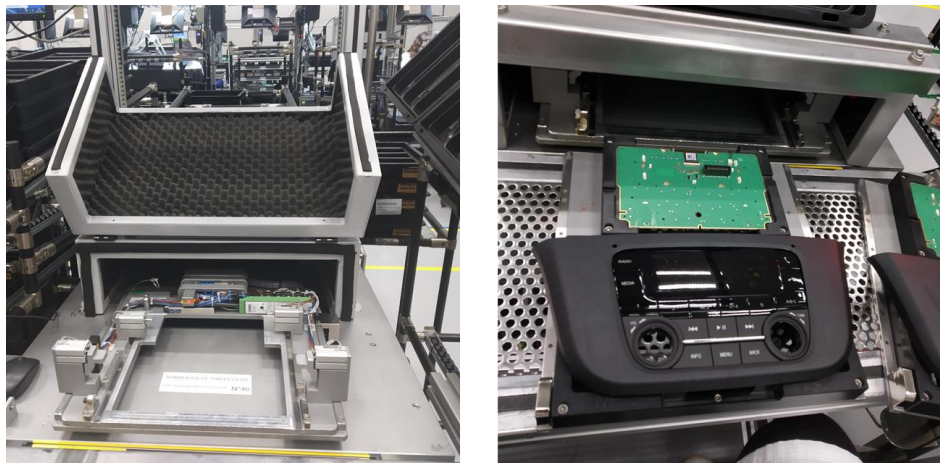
Máquina de limpeza do posto *sub-assembly* de blendas 1
